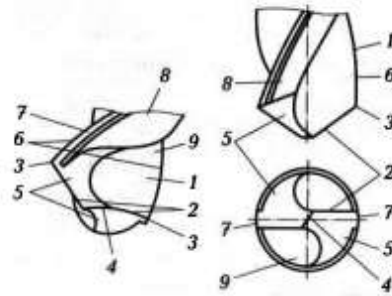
Поверхности и режущие кромки сверла спирального сверла:
